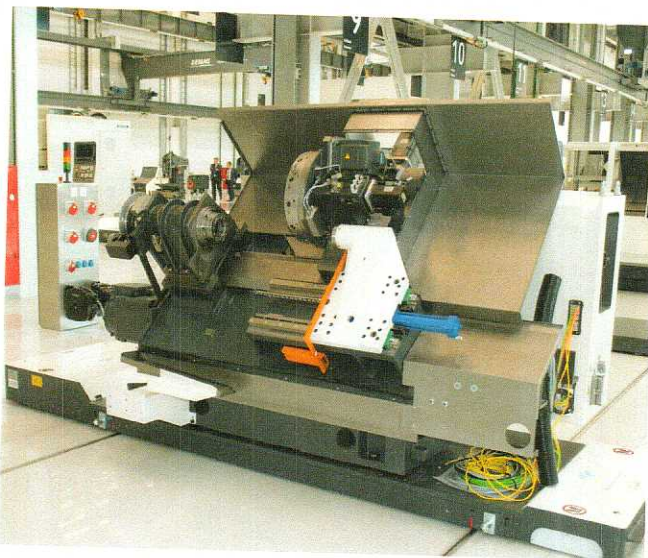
Компоновка станка DMG Mori. Показать расположение станины, шпиндельной бабки, револьверной головки, направляющих, задней бабки
